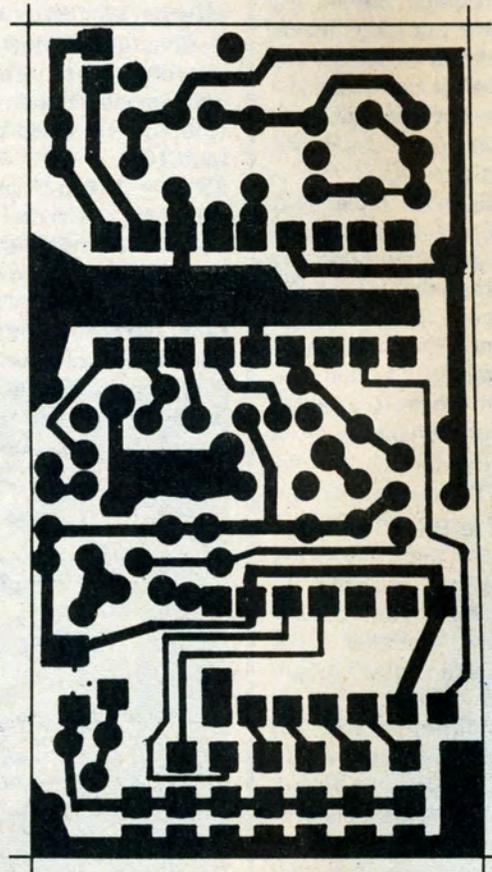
Négatif du plan de masse du RX 1872 B.
